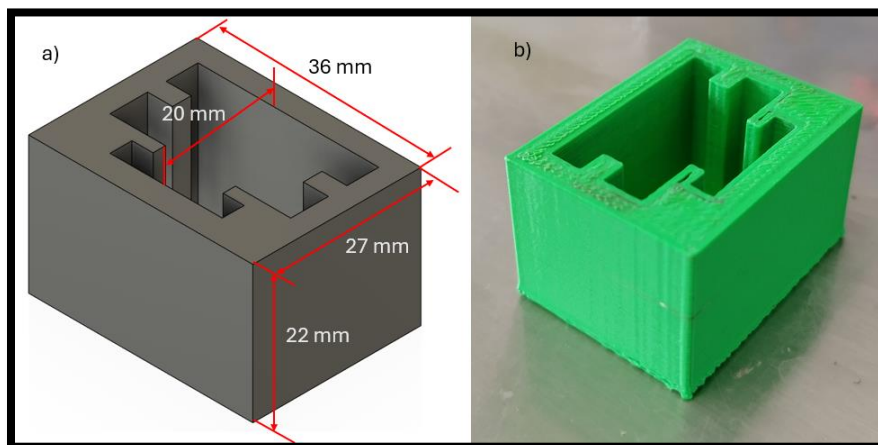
10. a) Diseño 3D de celda electrolítica, b) Impresión 3D de celda electrolítica.
